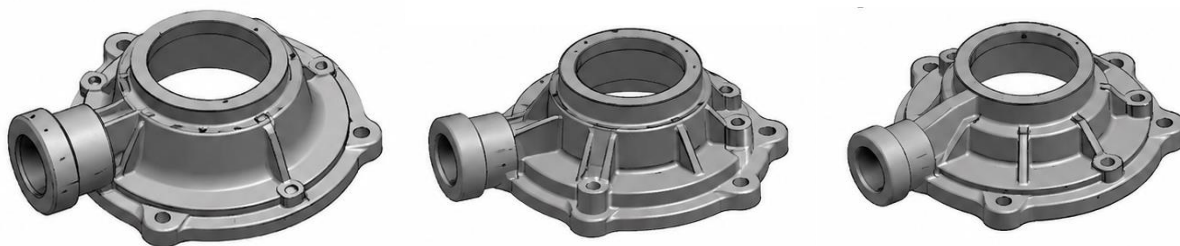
Загальний вигляд фланцевої корпусної кришки
